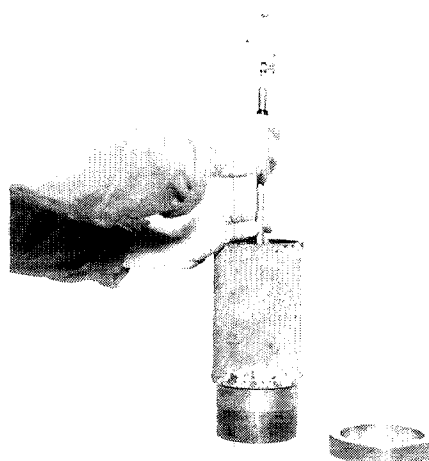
Nachmessen der Lauffläche einer Zylinderbüchse
